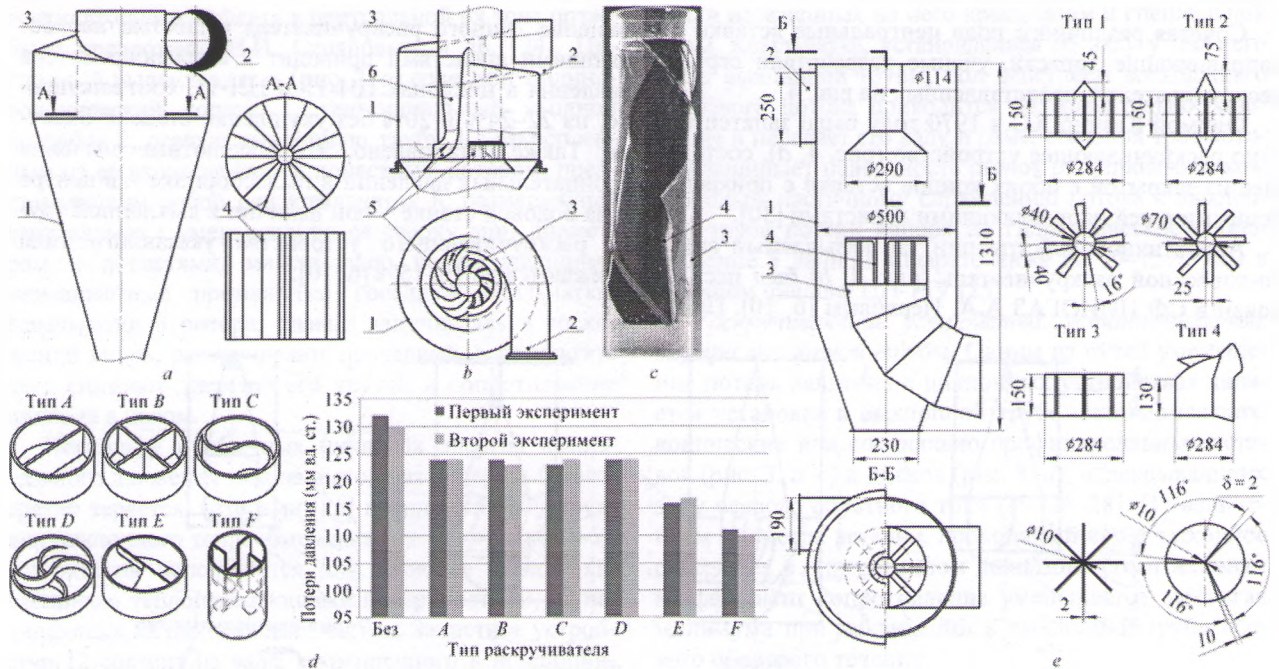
Раскручивающие устройства, устанавливаемые внутри выхлопной трубы: а – пластинчатый раскручиватель – звездочка [6]; б – устройство в виде турбины [37]; в – «винтовой диффузор» [38]; д – фирмы Samsung Gwangju Electronics Co [39]; е – розетки [40]; 1 – корпус; 2 – входной патрубок; 3 – выхлопная труба; 4 – раскручиватель; 5 – направляющие перегородки; 6 – расширяющийся канал
